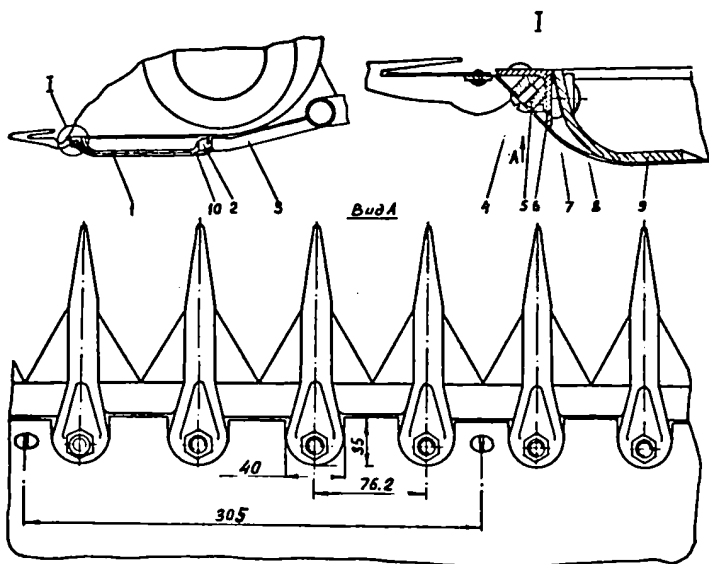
Режущий аппарат жатки, переоборудованной для низкого среза: 1 – опорный лист; 2 – кронштейн; 3 – угольник днища; 4 – винт; 5 – бобышка; 6 – пальцевый брус; 7 – косая шайба; 8 – болт; 9 – передний брус; 10 – угольник
